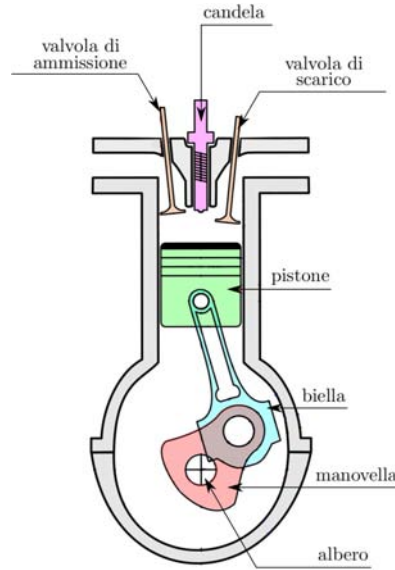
sezione del cilindro di un motore a combustione interna[34]
